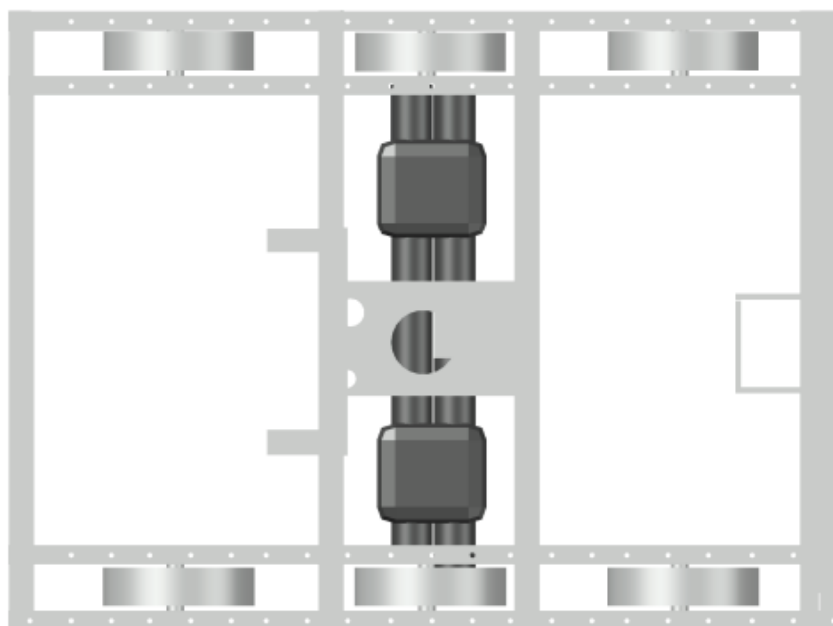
3D-модель платформы (вид сверху)
